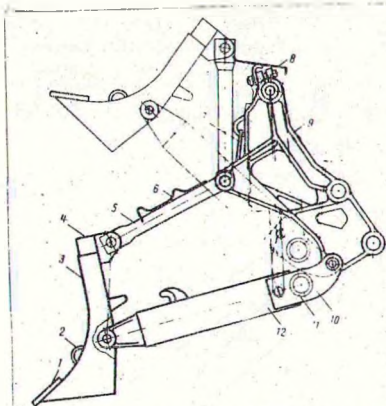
Толкатель с навеской трактора ТДТ-55: 1-нож; 2-буксирная скоба; 3-отвал; 4-балка; 5-тяги; 6, 8 -подножки; 7-скоба; 9-10-кронштейны; 11-труба; 12-рамка.
